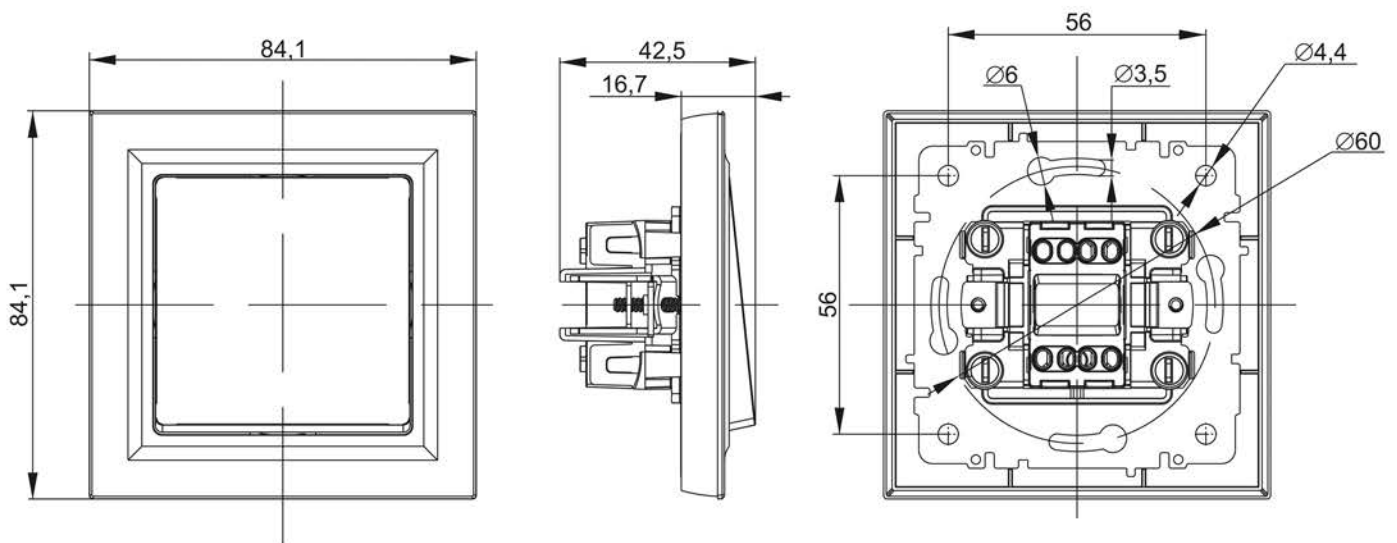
Габаритные и установочные размеры выключателей с рамкой / Figure 3 – Overall and mounting dimensions of switches with frame / 3-сурет – Жа қтауы бар ажыратқыштардың габаритті және орнату өлшемдері / Figura 3 – Dimensiunile și dimensiunile de instalarea a comutatoarelor cu cadru / Şəkil 3 – Çərçivə ilə açarların ümumi və quraşdırma ölçüləri / Նկար 3 – Շրջանակով ասջատիչների ընդհանուր և տեղադրման չափերը / ნახატი 3 – ჩარჩოიანი ამომრთველის გაბარიტული და საყენებელი ზომები / 3-сурет – Алкактуу өчүргүчтөрдүн көлөм жана орнотуу өлчөмдөрү / Расми 3-Андозаҳои умумӣ ва насбии калидакҳои бо ҷаҳорҷӯба / 3-rasm – Ramka bilan viklyuchatellarning gabaritli va o'rnatishdagi o'lchamlari
